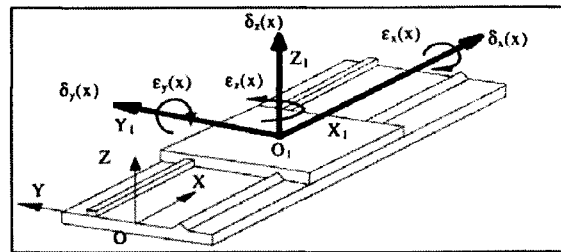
Esquemático de 6 componentes de error de movimiento de un carro de una máquina herramienta.
